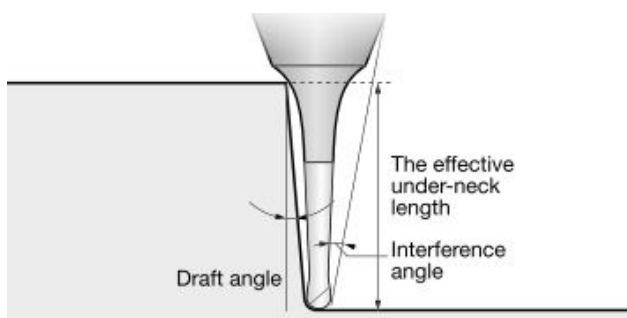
Miniaturní fréza EPDBPE [12]
